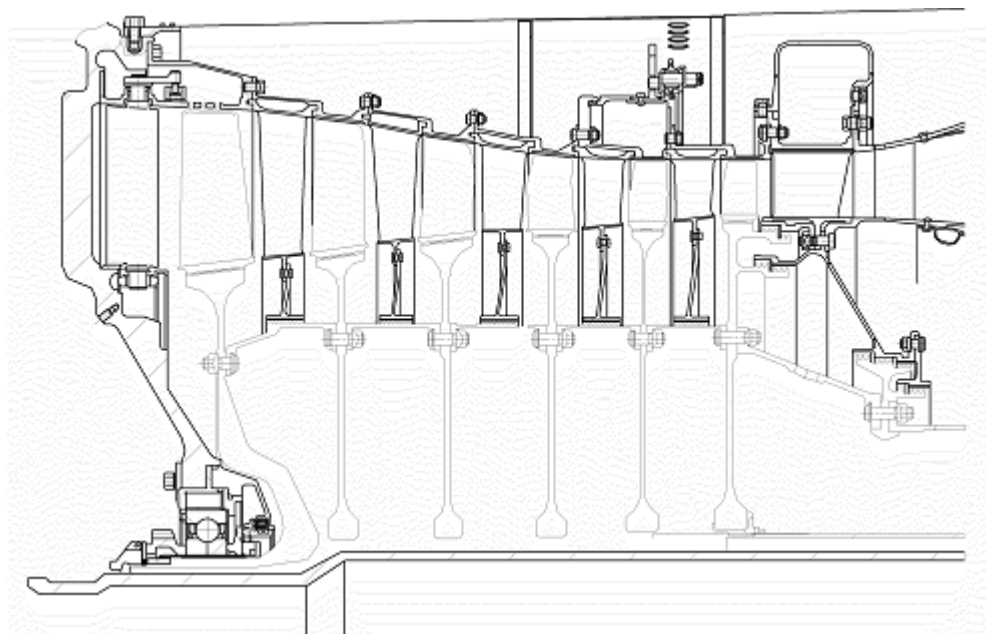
Корпус с поперечными разрезами компрессора ВД ТРДД НК-8
